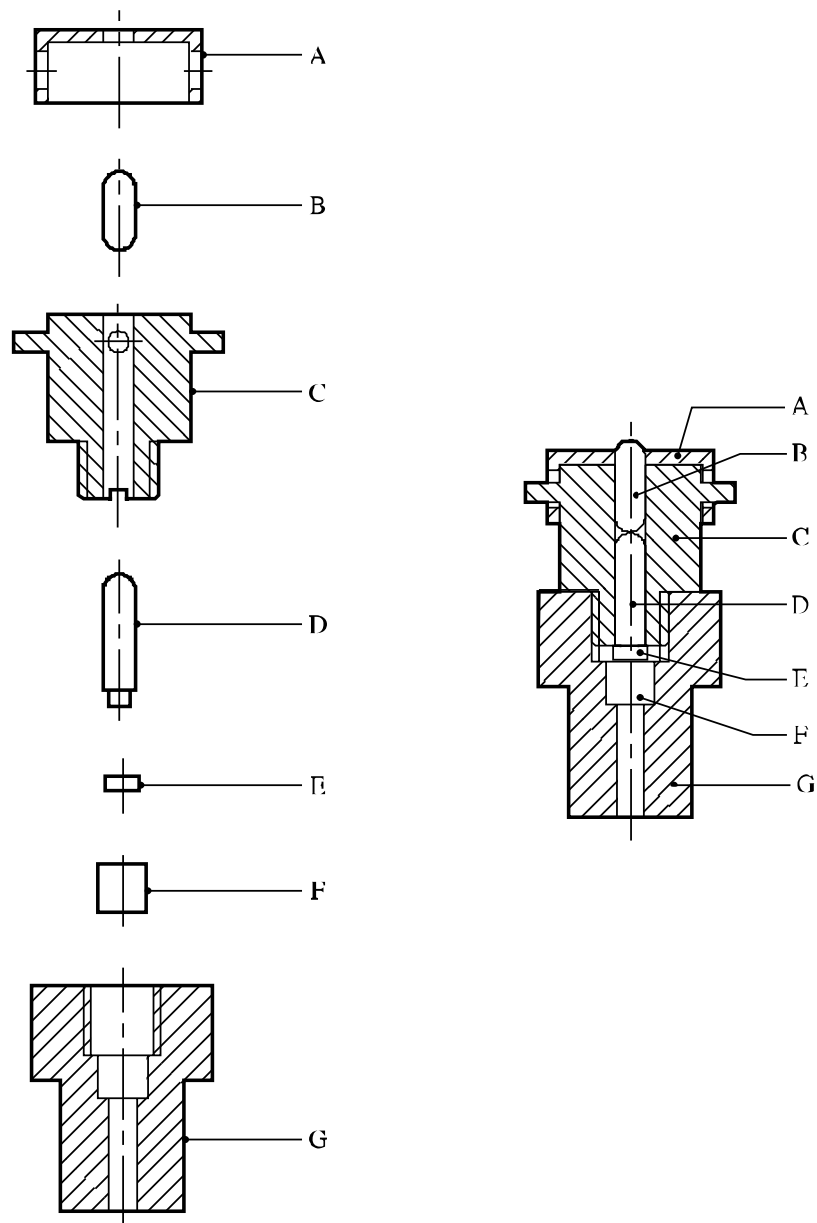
MOUTON DE CHOC DU "BUREAU OF EXPLOSIVES"
